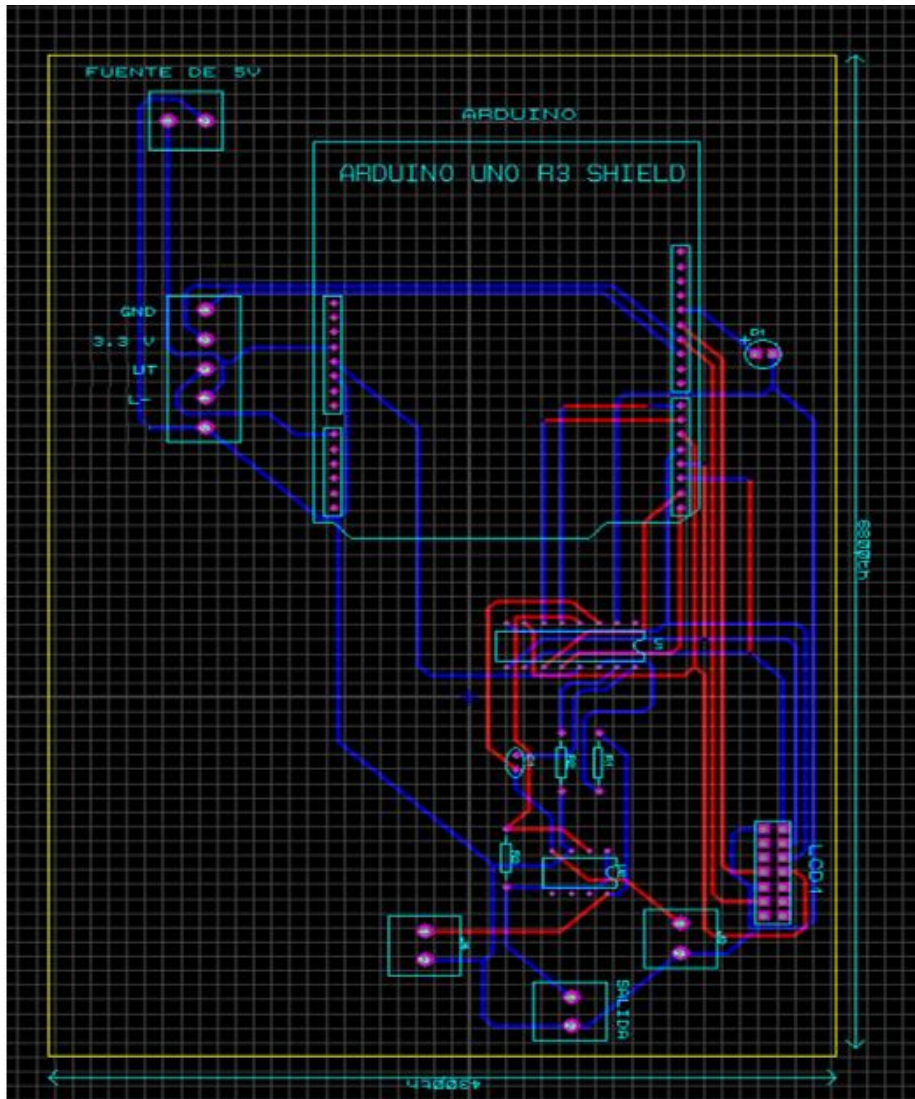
Diseño del PCB Arduino y Sensor de Presión MIK-P300
